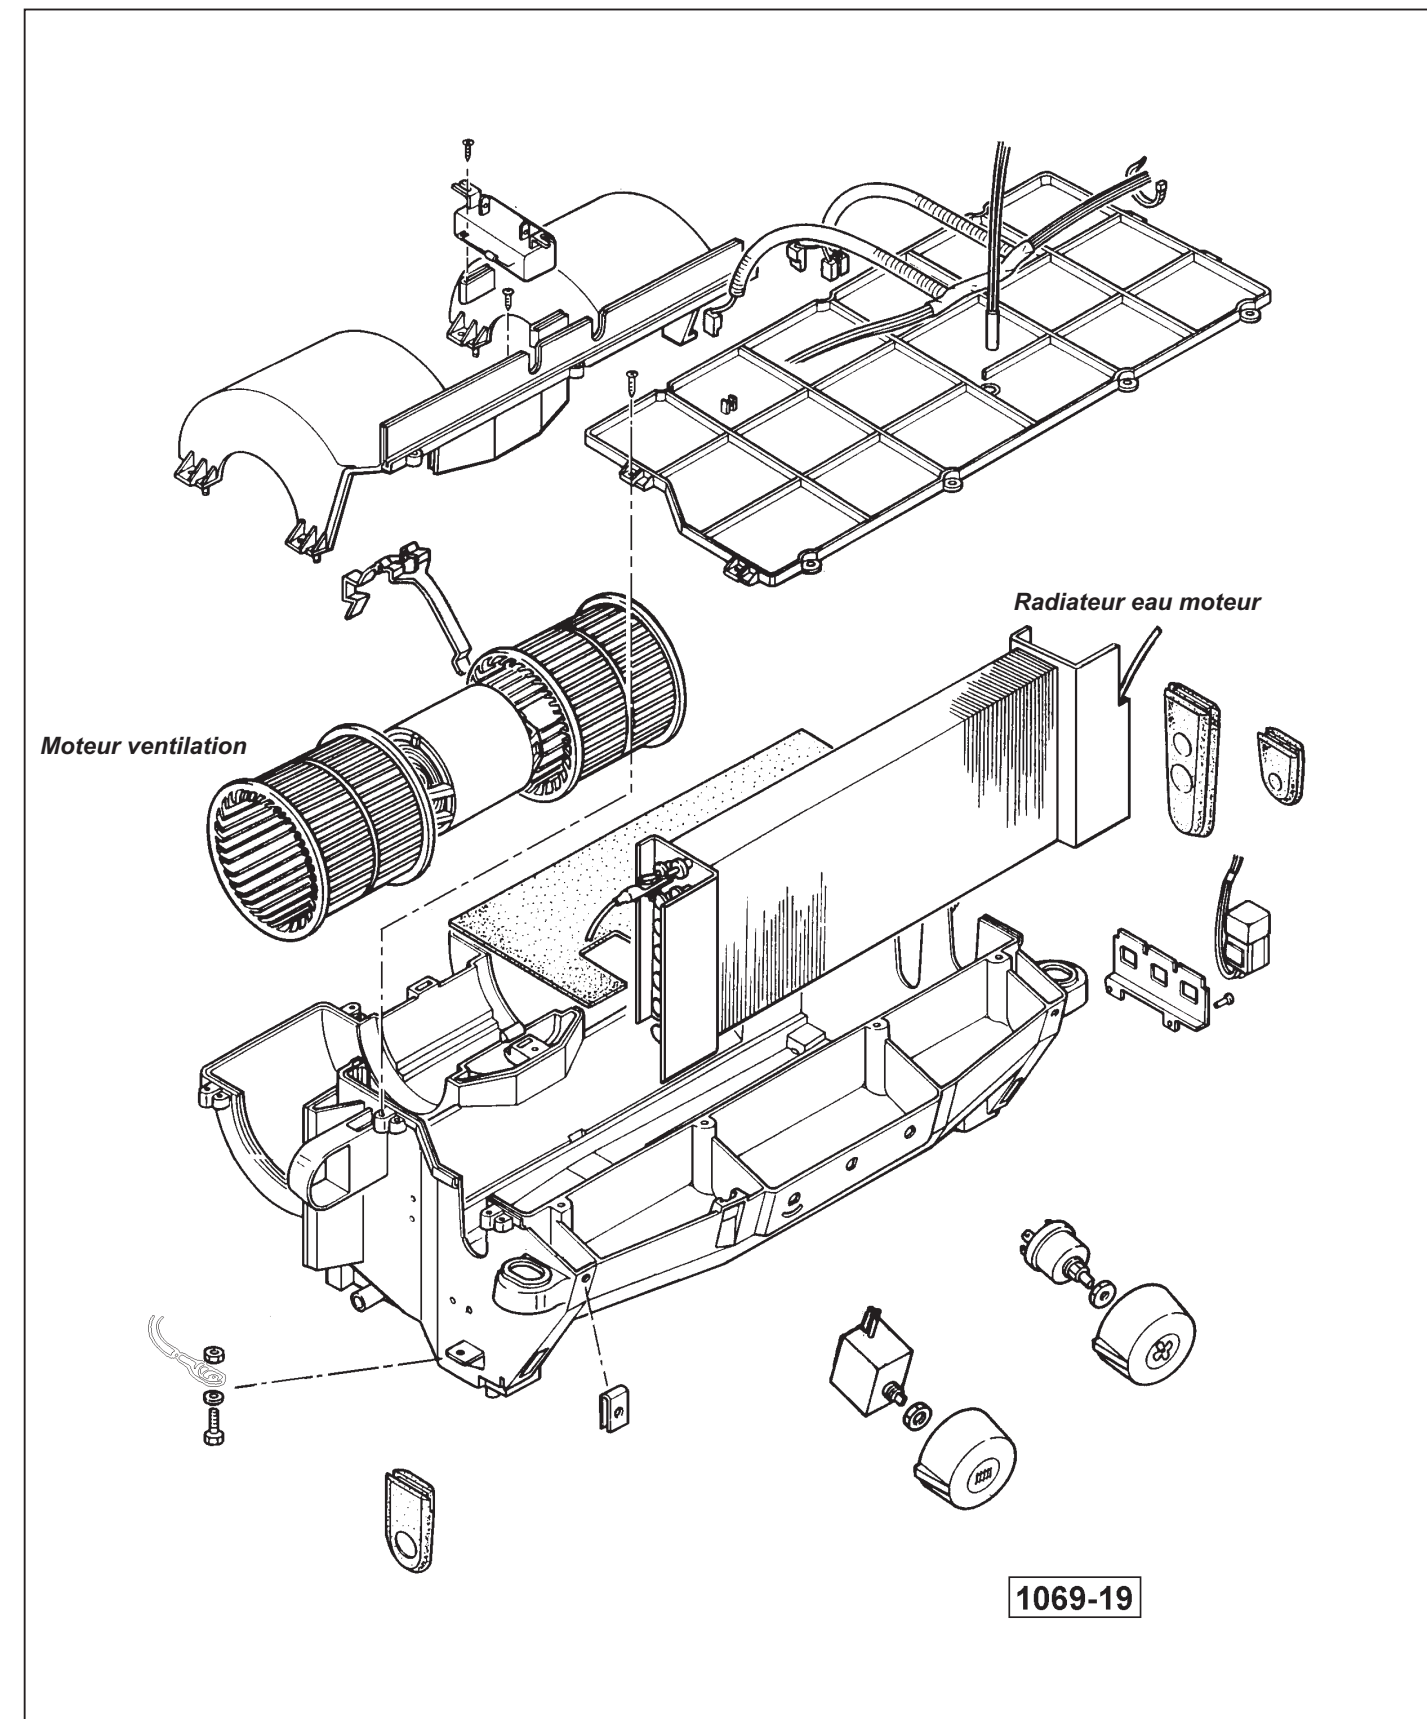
Eléments constitutifs du dispositif de ventilation - conditionnement d'air - chauffage.
